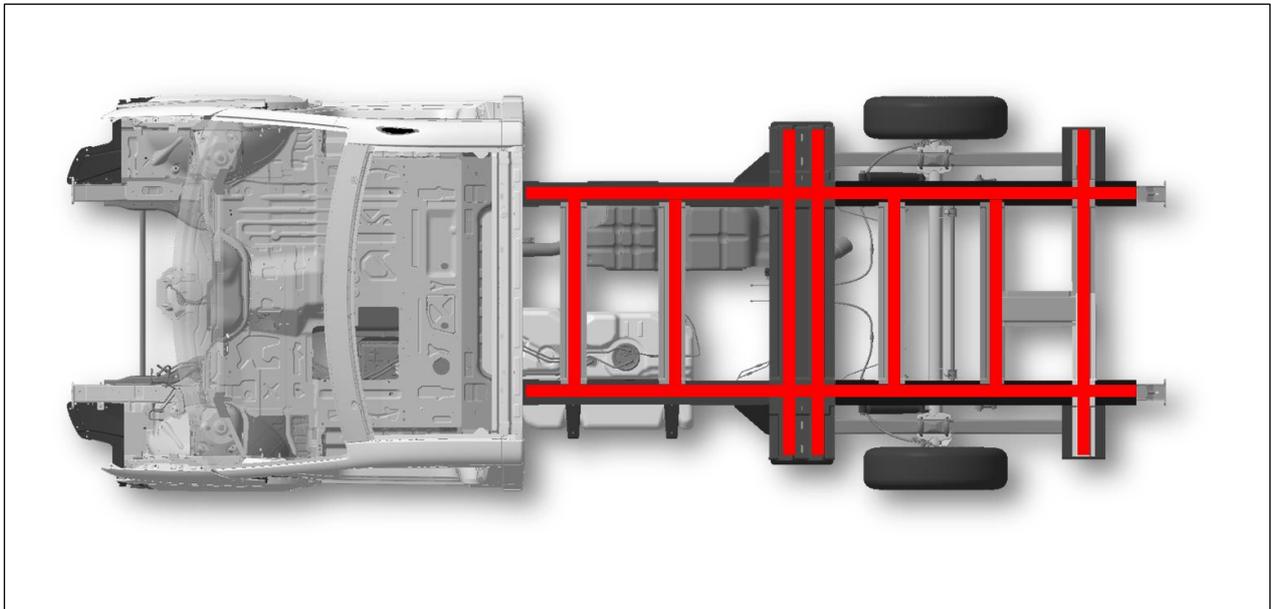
Châssis à cadre plat Crafter – Surfaces de collage pour superstructure (schéma de principe de la surface du cadre)
